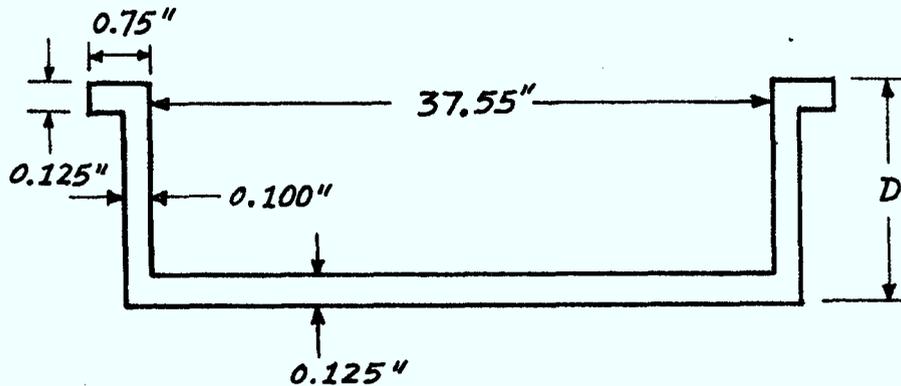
Détails des dimensions de la cavité (en pouces)
